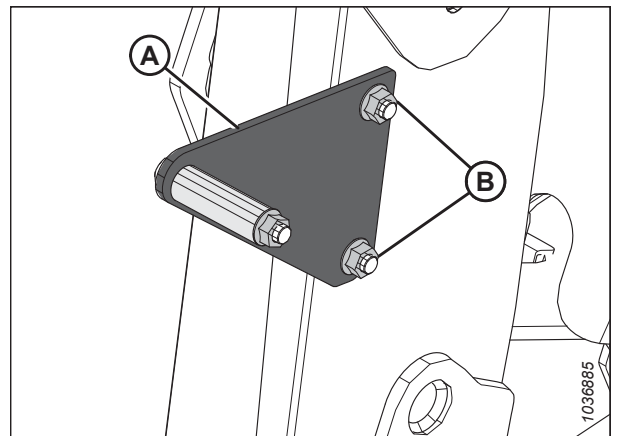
Кронштейн формовочного щитка — жатка R85
